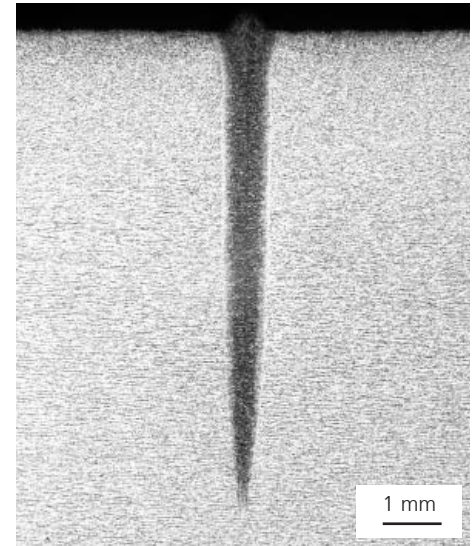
Querschnitt einer Laserstrahlschweißnaht (Parameter: YLR4000; P = 4 kW; v = 4 m min⁻¹; f = 300 mm; t_s = 8 mm)
